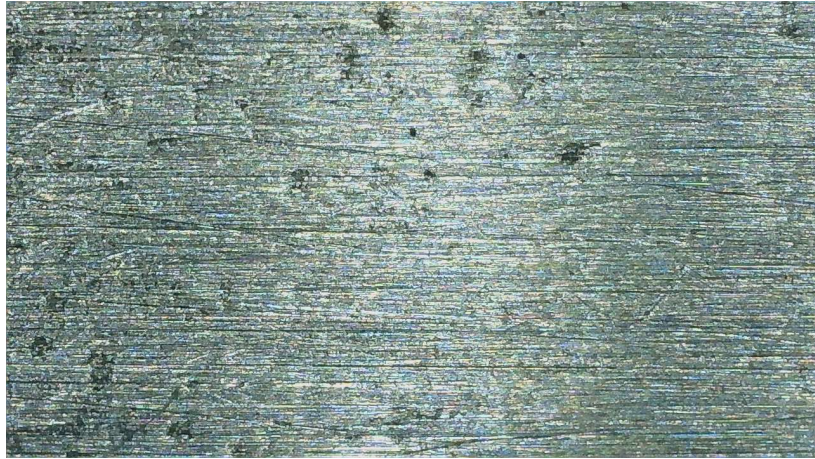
Plat Baja ST-37 Dilas Zig-Zag 100A
